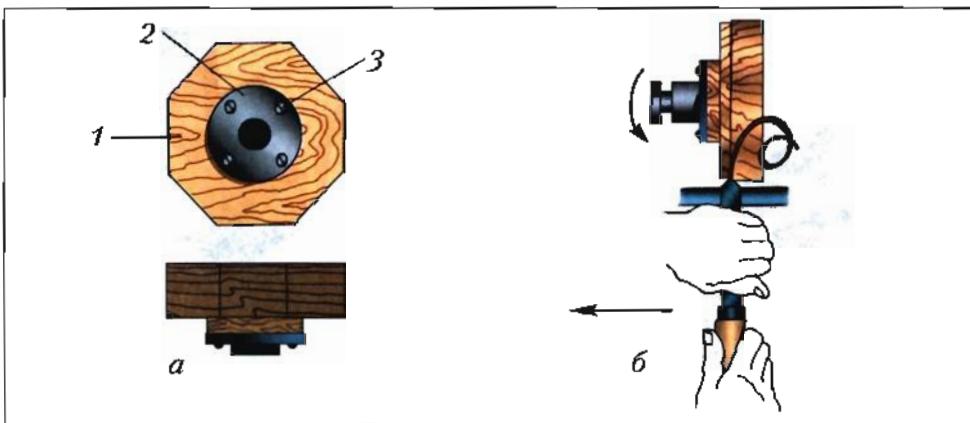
Крепление (а) и точение (б) заготовки на планшайбе:
